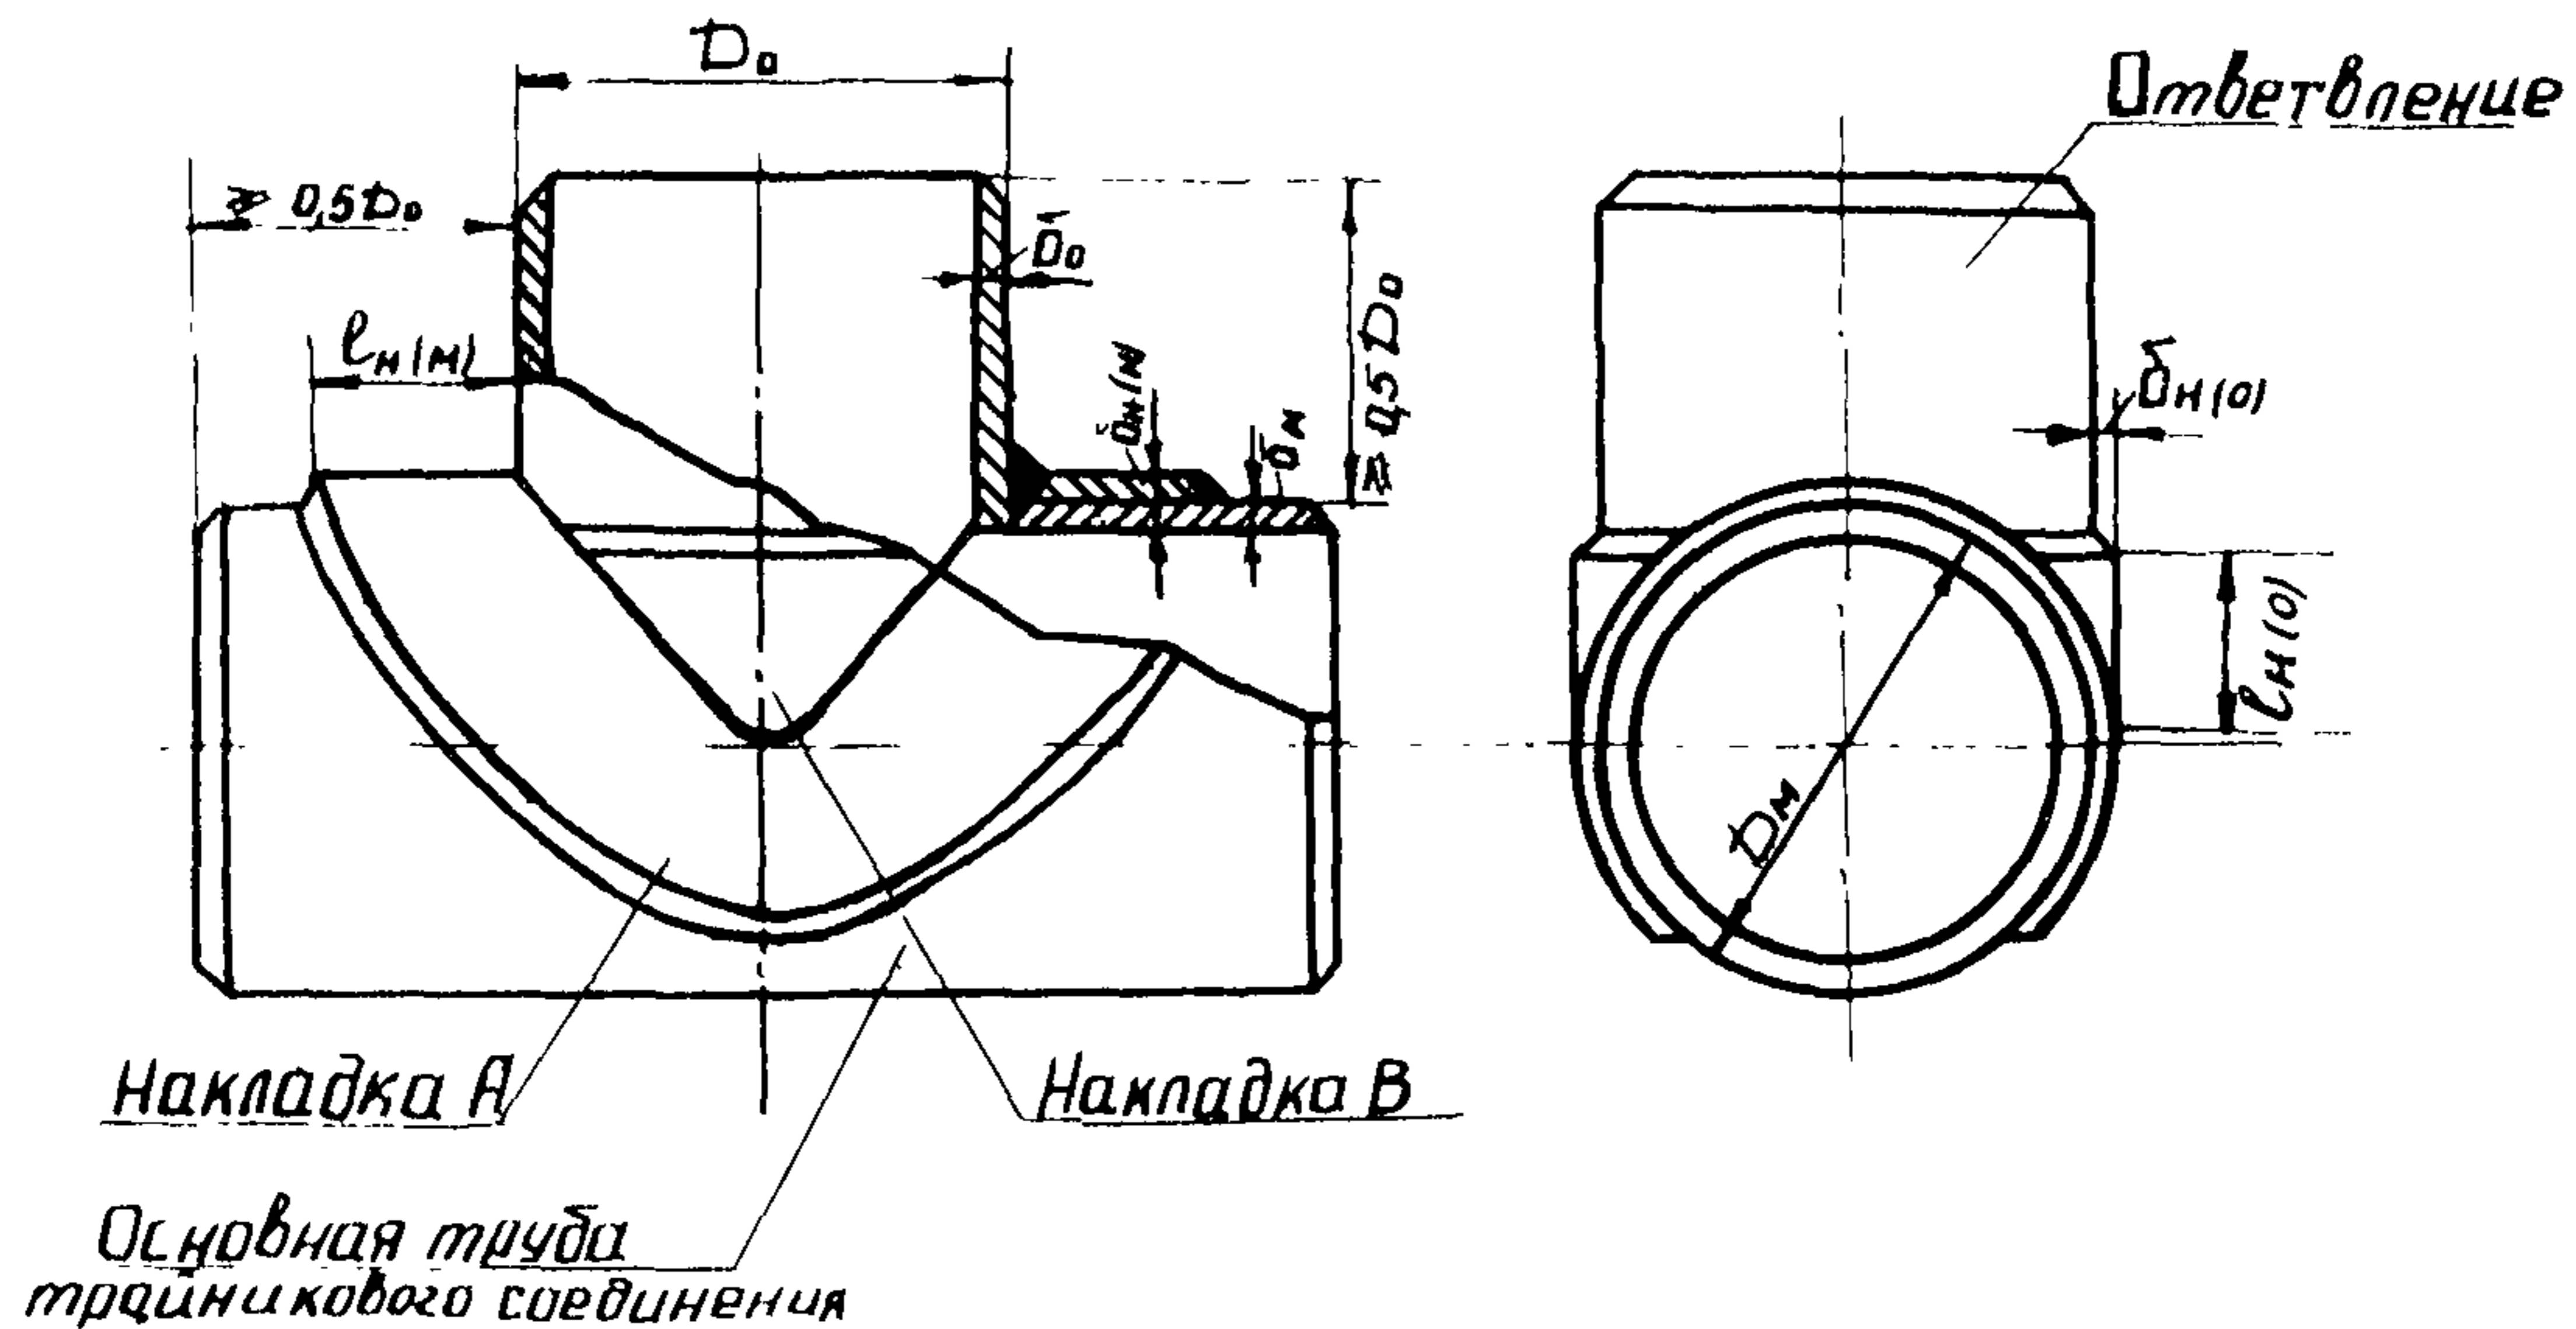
п. Сварной тройник, усиленный накладками
